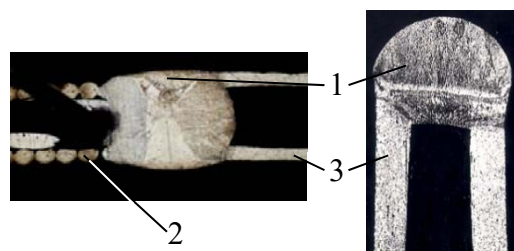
макроструктура сварных соединений а) шва №2; б) герметизирующего шва №3: 1 — сварной шов; 2 — гибкий трос; 3 — корпус
